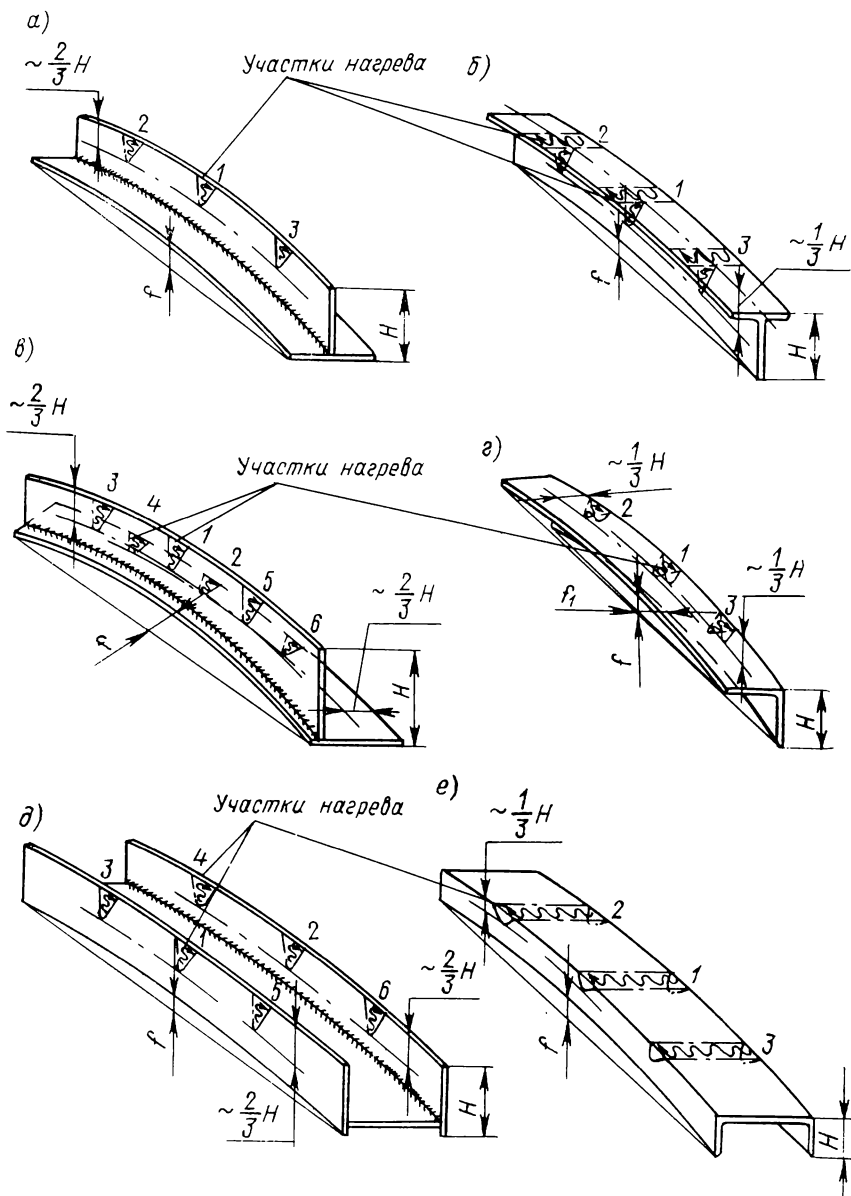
Схема правки продольного изгиба сварных и катанных балок: а, в, д — в случае изгиба на пояс; б, г, е — при изгибе на стенку. 1, 2, 3... — очередность нагрева.
